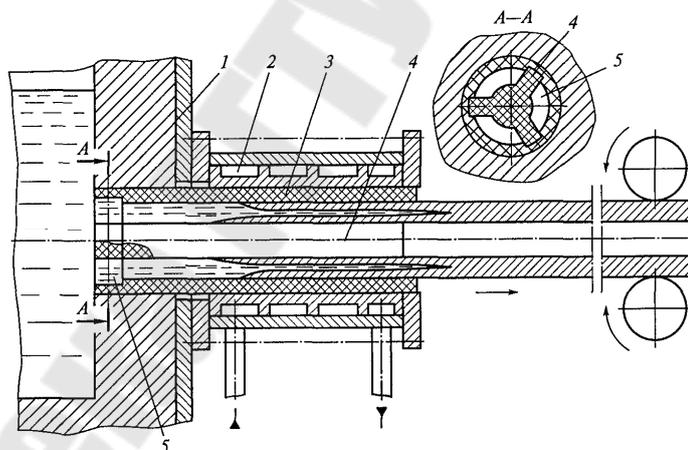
3 Схема кристаллизатора для горизонтального непрерывного литья трубчатых заготовок и профилей: 1 – раздаточная печь; 2 – водоохлаждаемая рубашка; 3 – графитовый вкладыш; 4 – стержень; 5 – отверстие для подвода расплава
